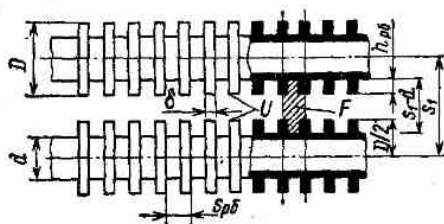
Схема к расчету труб с поперечными ребрами
